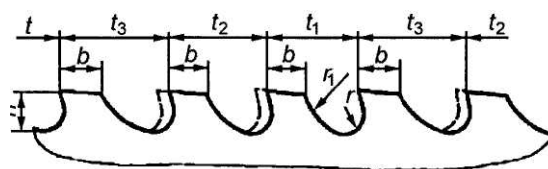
Эскизы к определению шагов чистовых зубьев круглых протяжек групповой схемы срезания припуска
